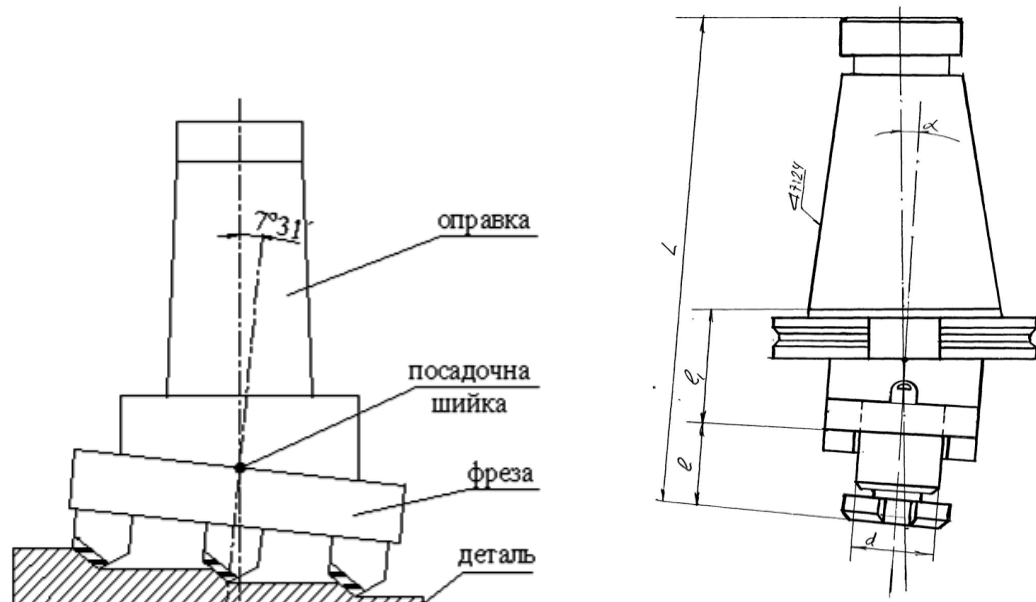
Схема прогресивного процесу фрезерування поверхні деталі та ескіз спеціальної оправки для фрези-протяжки
